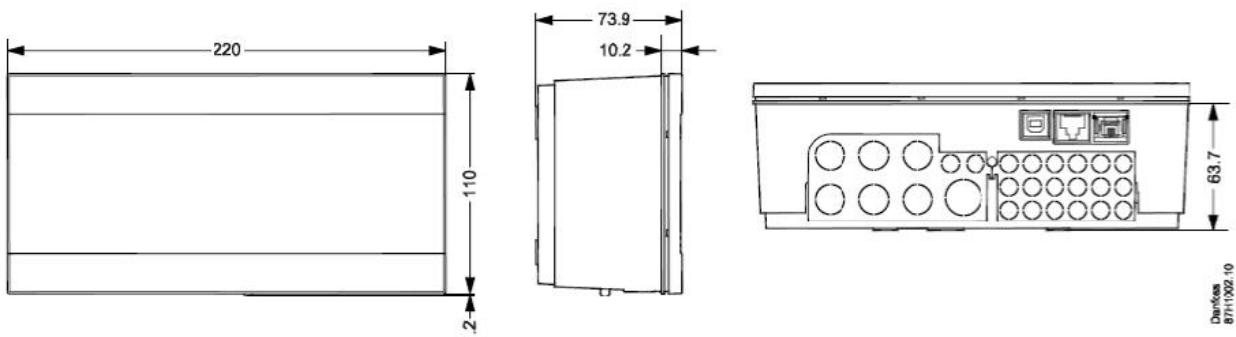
Габаритные и присоединительные размеры ECL Comfort 310B.
